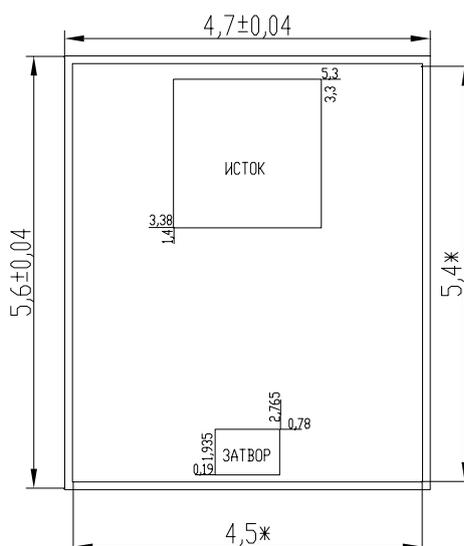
Габаритный чертеж кристалла 2П771А-5
